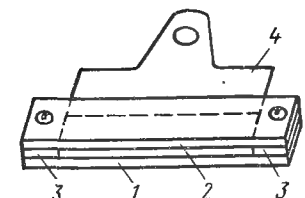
Приспособление для отбортовки манжеты пазовой коробочки:
